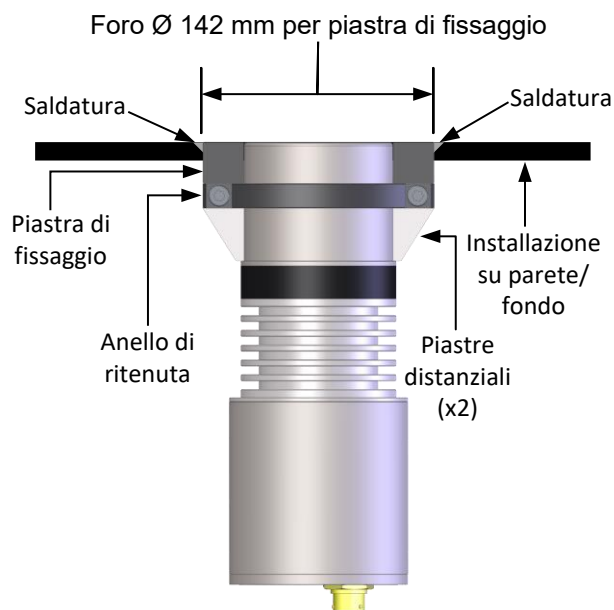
Installazione del sensore (piastra di fissaggio montata a filo)
